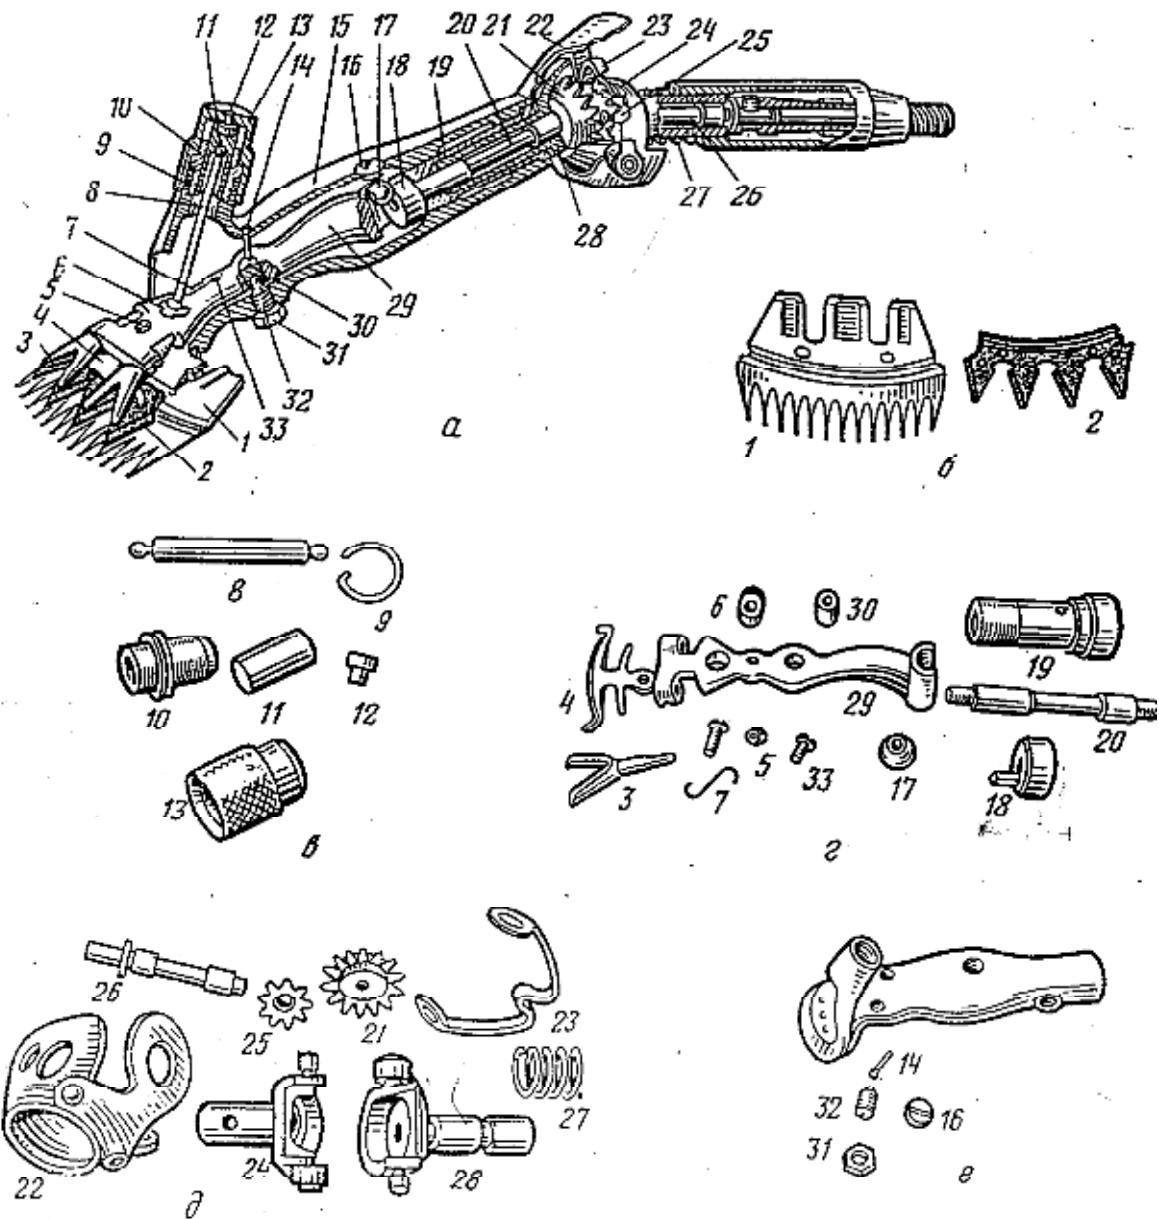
Общий вид (а) машинки МСО-77Б для стрижки овец и детали режущего аппарата (б), нажимного (в), эксцентрикового (г), шарнирного (д) механизмов и корпуса (е): 1 - гребенка; 2 - нож; 3 - нажимная лапка; 4 - пружина нажимных лапок; 5 - гайка; 6 - подпятник стержня; 7, 27 - пружины; 8 - упорный стержень; 9 - стопорная пружина; 10 - штуцер; 11 - нажимной патрон; 12 - упор патрона; 13 - нажимная гайка; 14 - предохранительный винт; 15 - корпус; 16 - заглушка; 17 – ролик; 18 — эксцентрик; 19 - втулка; 20 - валик; 21 - большая шестерня; 22 - наружный кожух; 23 - замок шарнира; 24 -
